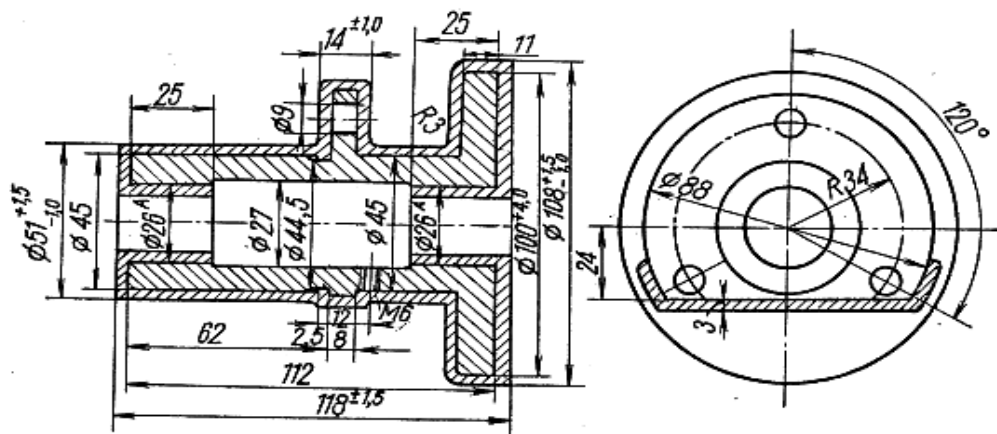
Заготовка чавунної втулки у вигляді виливка
